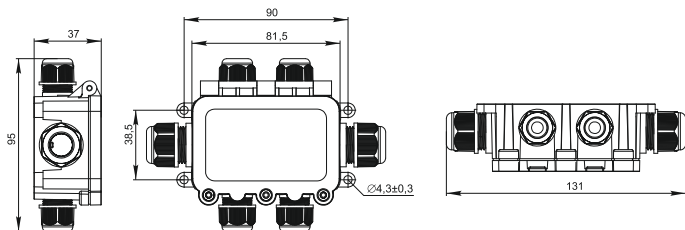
Габаритные размеры коробки WTP-405 / Figure 5 – Overall dimensions of the WTP-405 box
